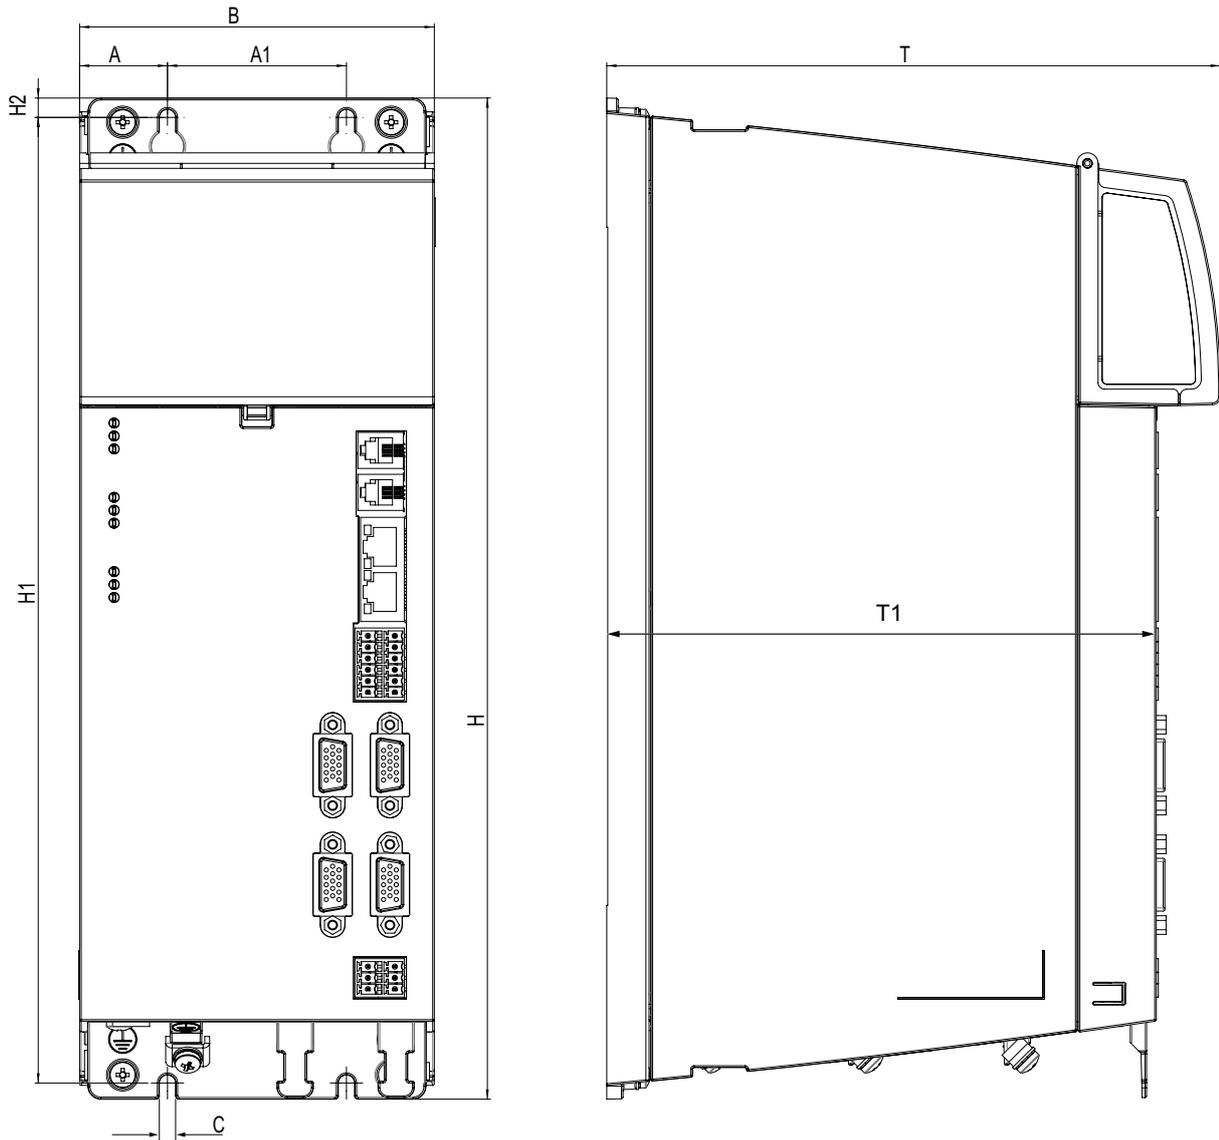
Maßzeichnung JM-3000 Servoverstärker BG2 Cold Plate (Maße siehe Tabelle 2.2)
